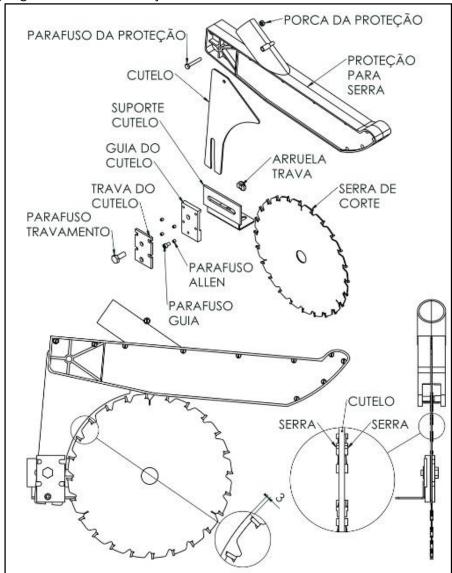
REGULAGEM CONJUNTO PROTEÇÃO DA SERRA
